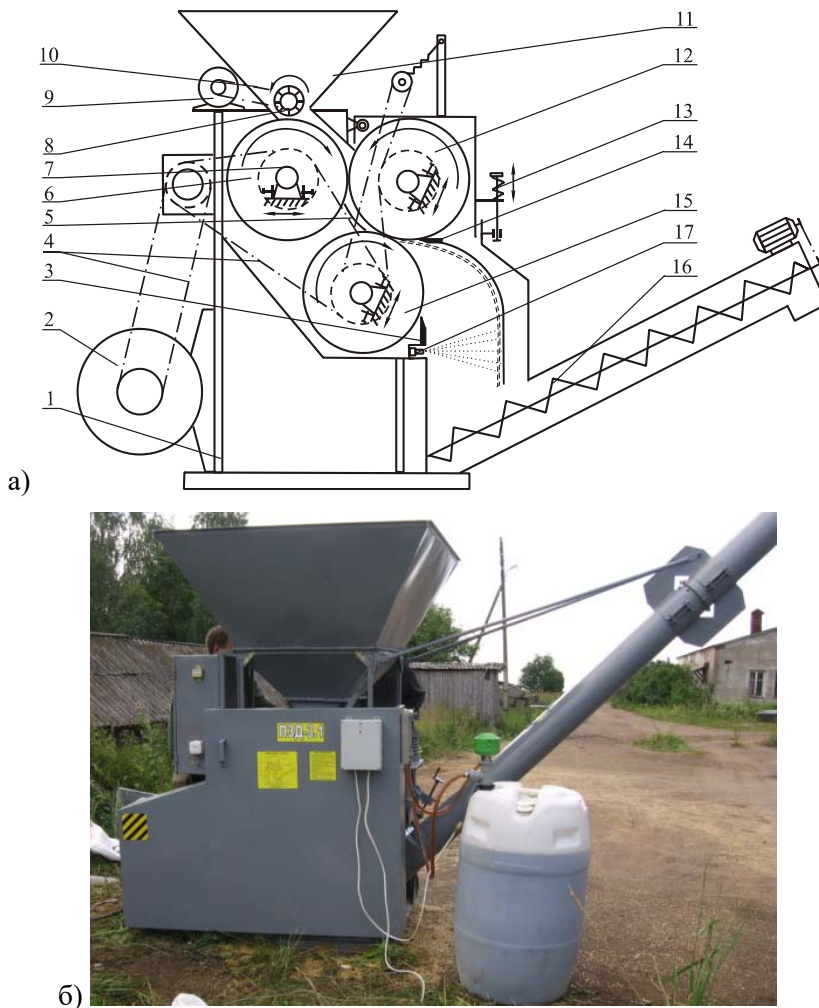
Плющилка зерна ПЗД-3: а) конструктивно-технологическая схема, б) общий вид; 1 = рама; 2 = электродвигатель; 3 = очищающий нож; 4 = цепная передача; 5 = очищающий нож-направитель криволинейной формы; 6 = основной валец; 7 = регулируемая опора; 8 = питающее устройство; 9 = электродвигатель; 10 = цепная передача; 11 = питательный бункер; 12 = боковой валец; 13 = защитное устройство; 14 = очищающий нож; 15 = нижний валец; 16 = выгрузной транспортер; 17 = форсунка; источник: собственное исследование
